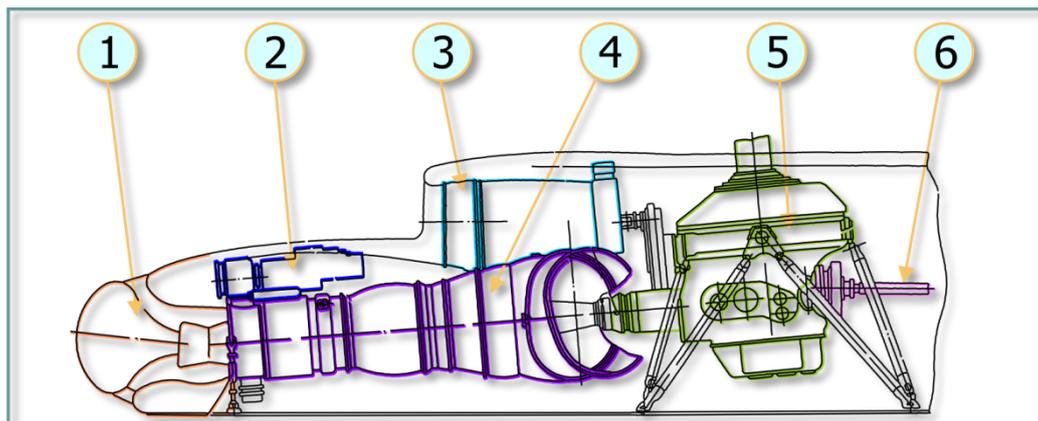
Схема расположения агрегатов силовой установки (вид сбоку):
